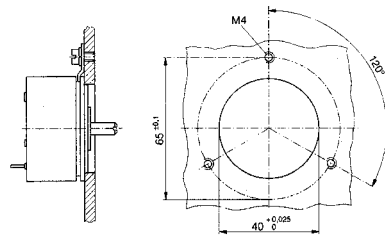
Bohrplan für Befestigung mit 3 Spannkammern.
